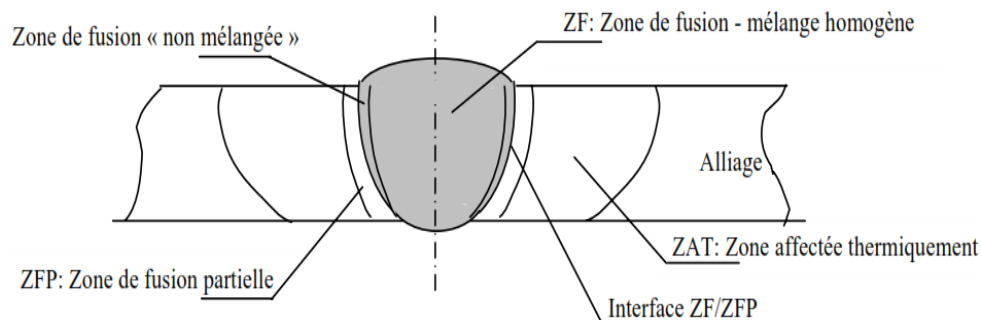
Zones principales d'une soudure par fusion.
